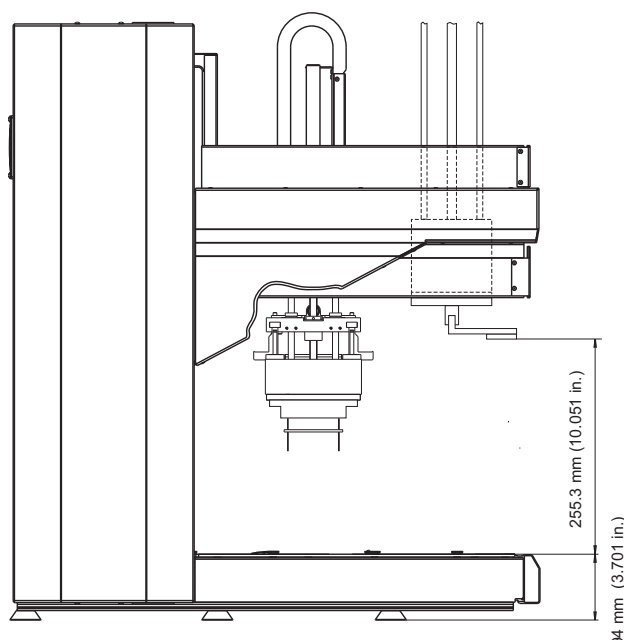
spazio di lavoro della pinza del braccio MCA384 (distanza dal piano di lavoro)
